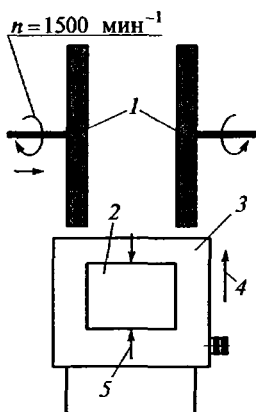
Схема полуавтомата для зачистки двух торцов корпусных отливок средних размеров: 1 — шлифовальные круги; 2 — отливка; 3 — стол; 4 — направление подачи отливки; 5 — зажим отливки; n — скорость вращения шлифовальных кругов
